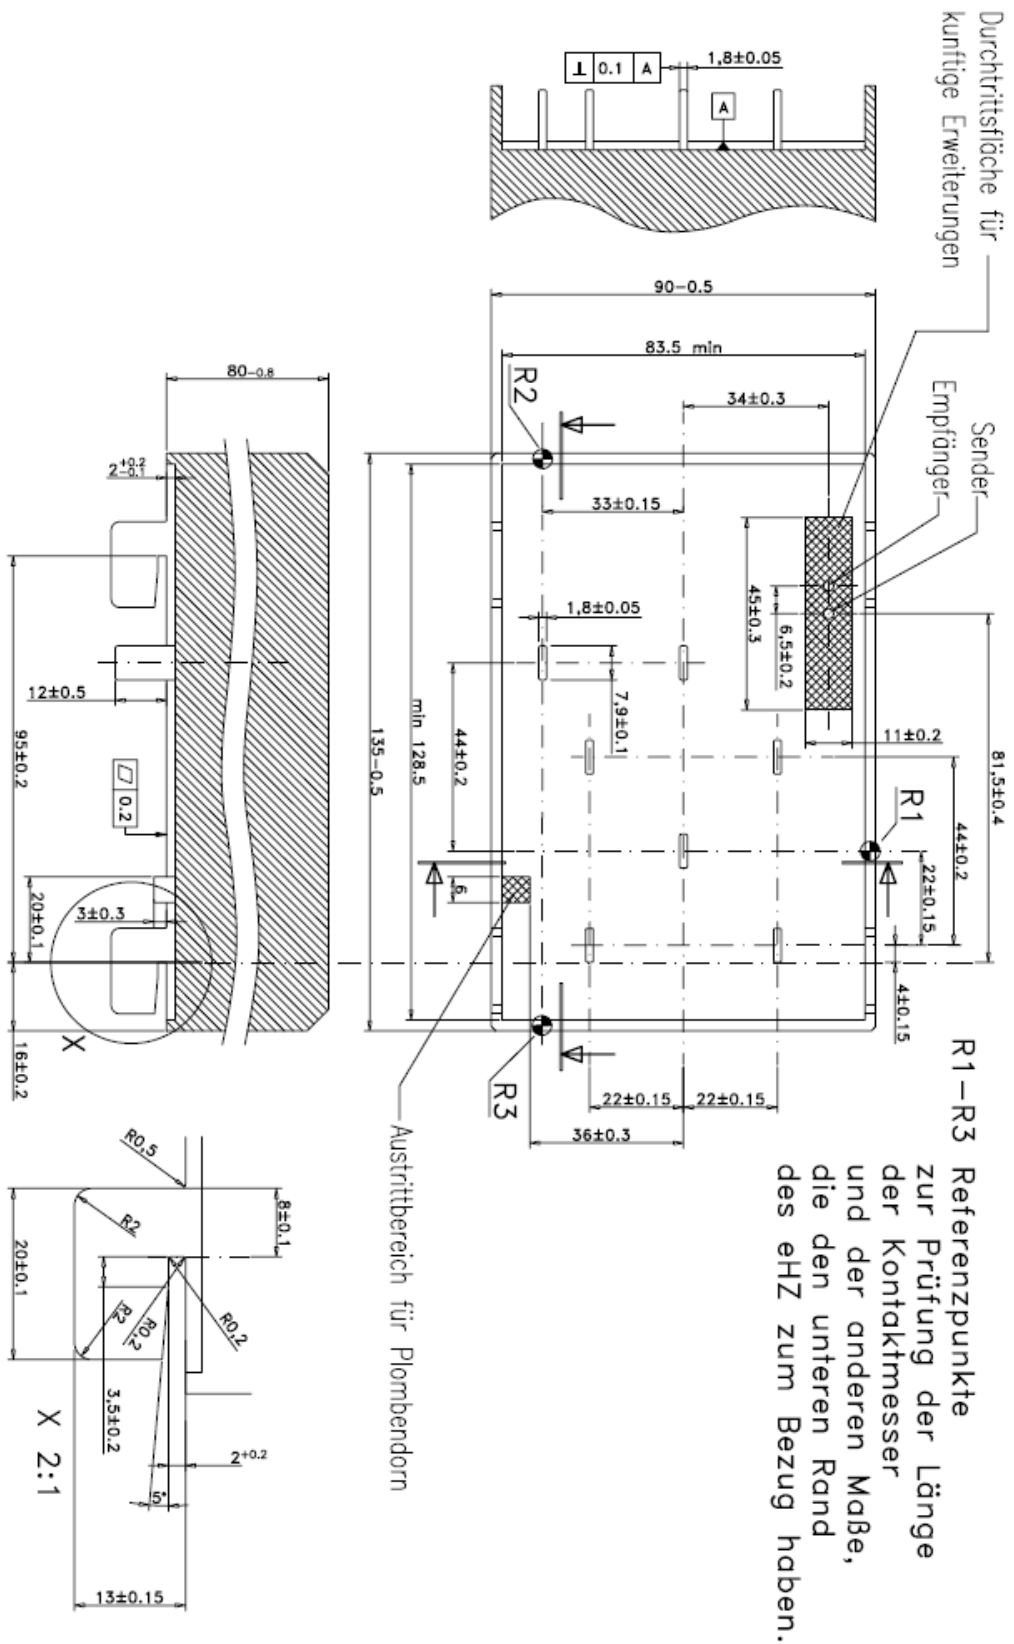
Rückansicht, Zeichnung mit Maßen (druckbedingt nicht maßstabsgerecht) [KGB_0094]
